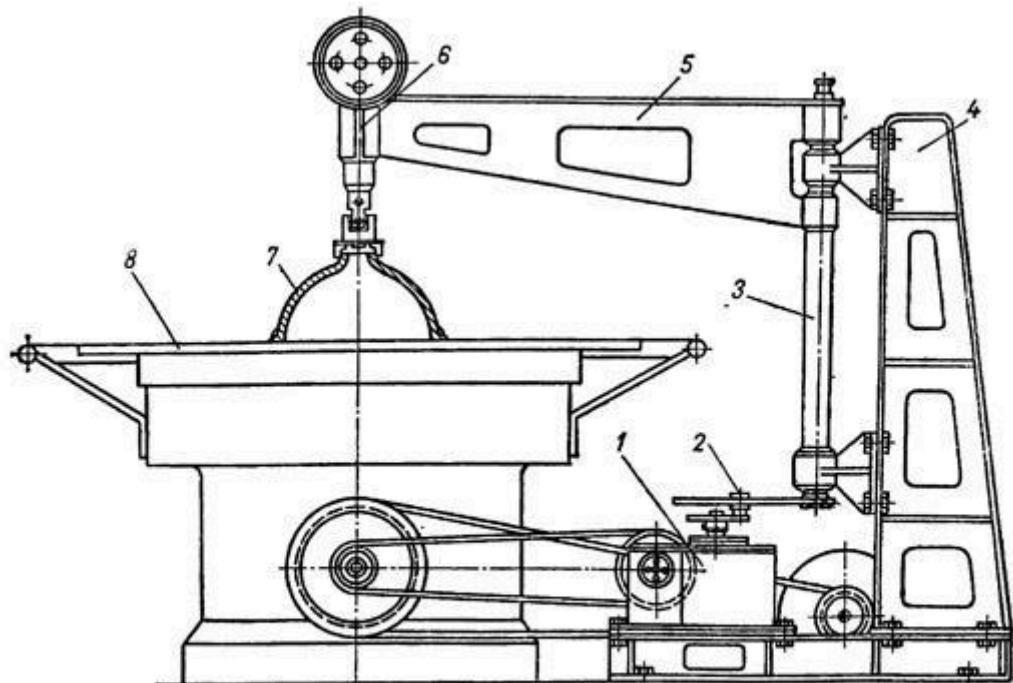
Притиальній верстат з пристроєм для механічного переміщення деталі, що притирається.
